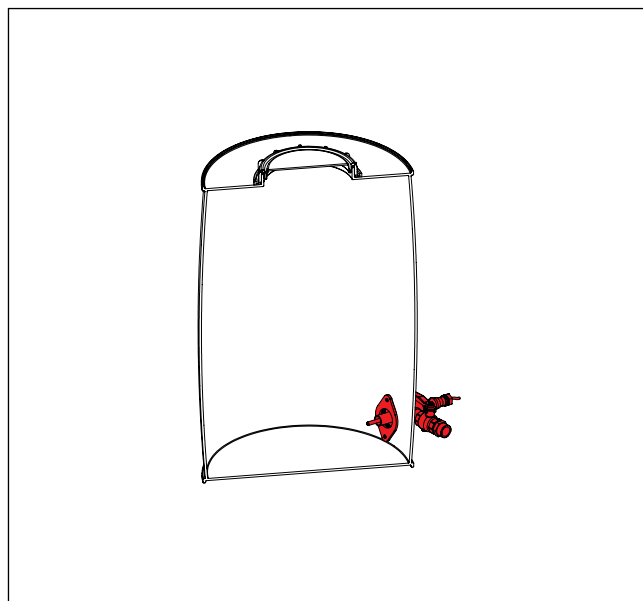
Einbau Ovalflansch innen und Behälteranschluss-Einheit waagrecht
